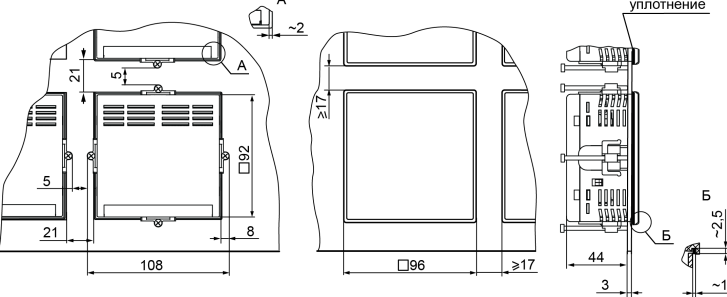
Корпус Щ1 в щите толщиной 3 мм
